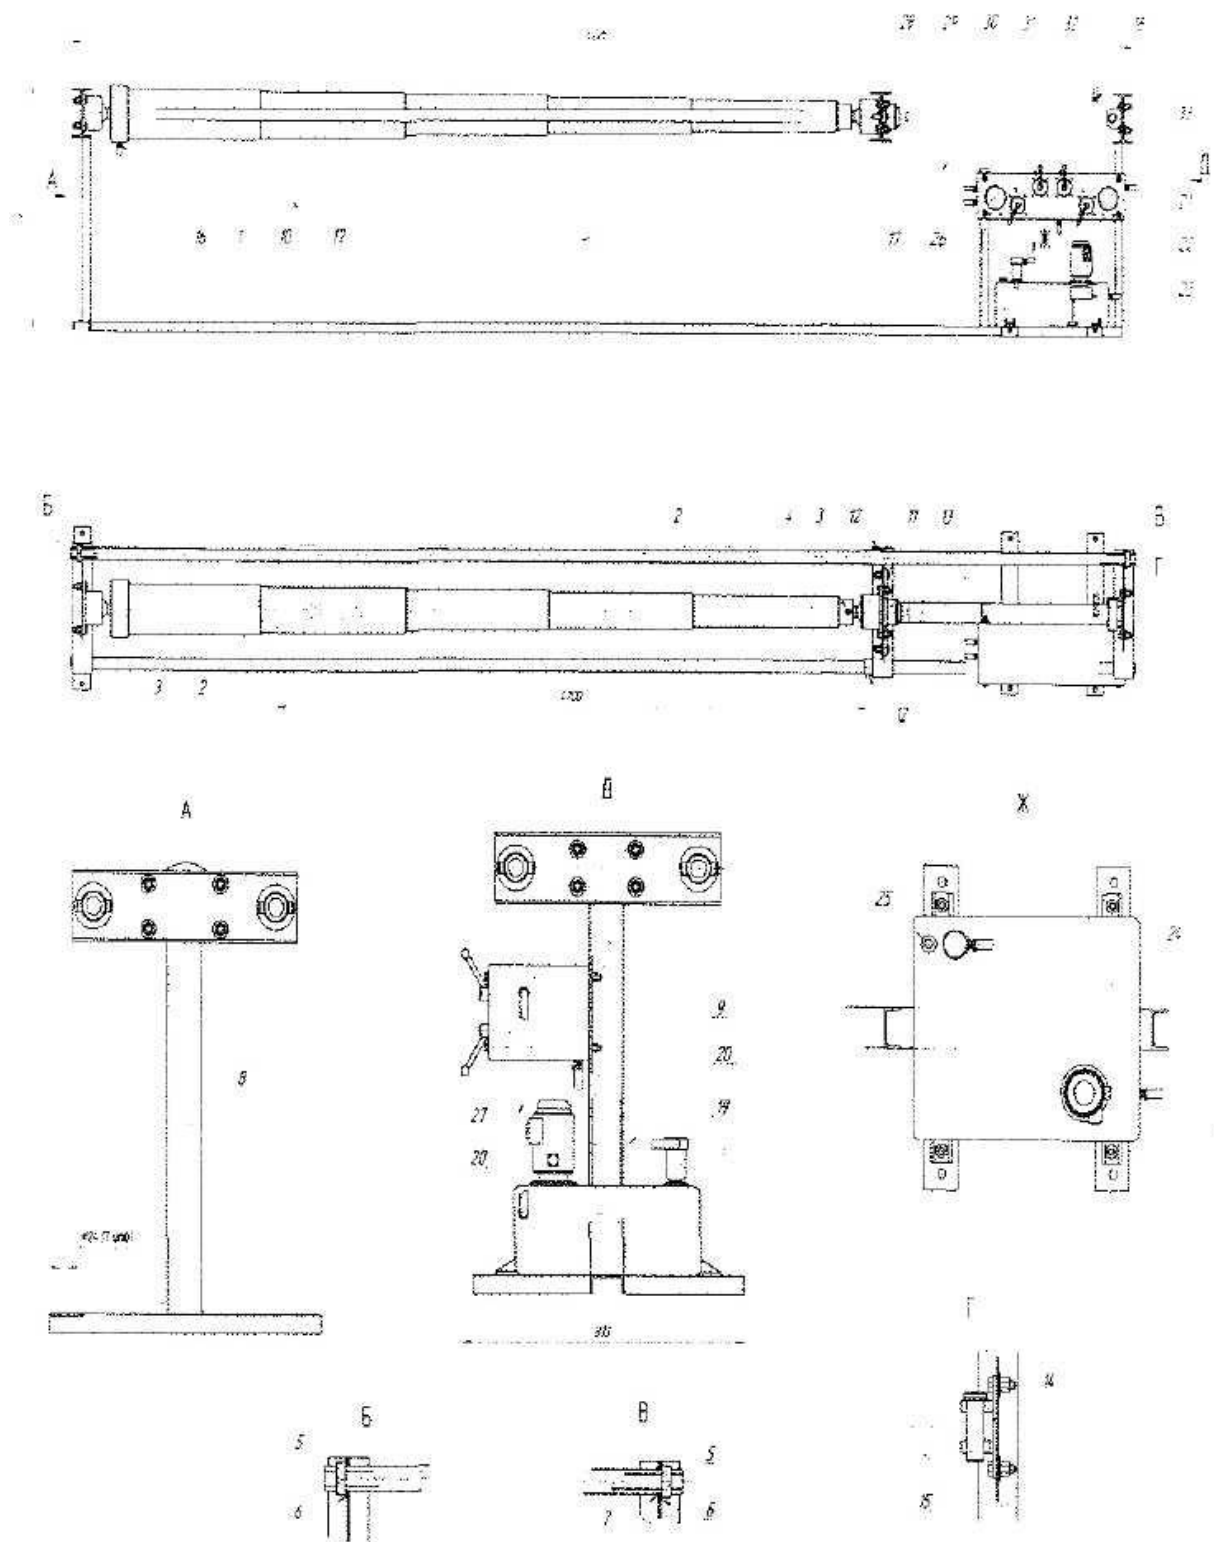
Конструкция проектируемого стенда для проверки гидравлических цилиндров
